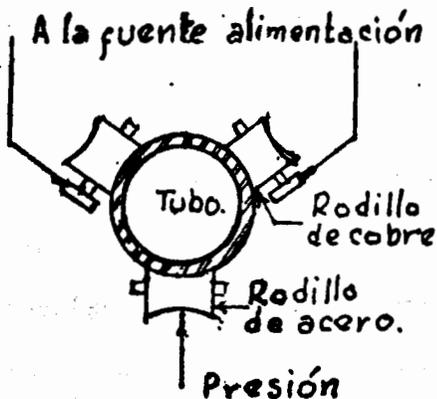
SOLDADO DE TUBOS POR RECALCADO.
